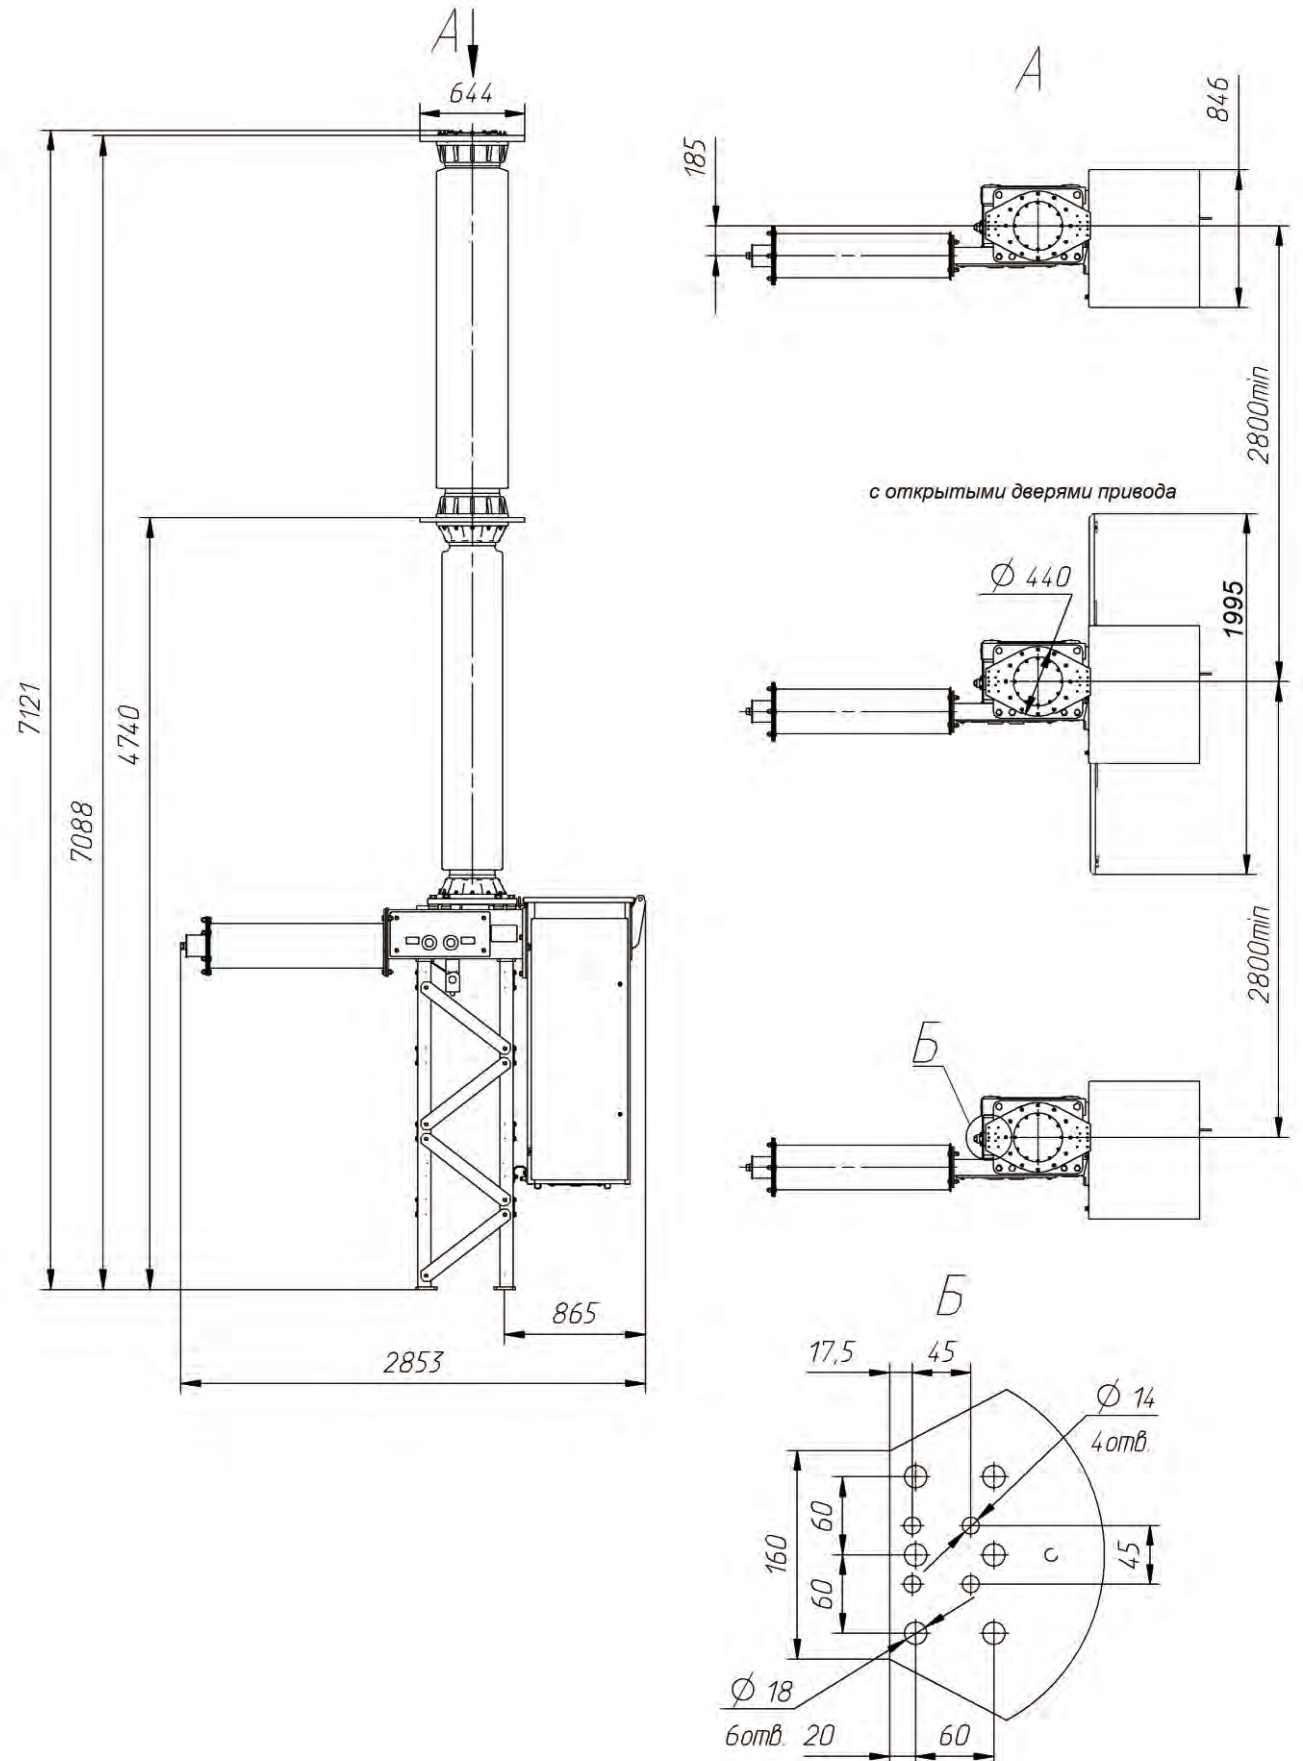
Однополюсное исполнение с заводскими опорными металлоконструкциями
